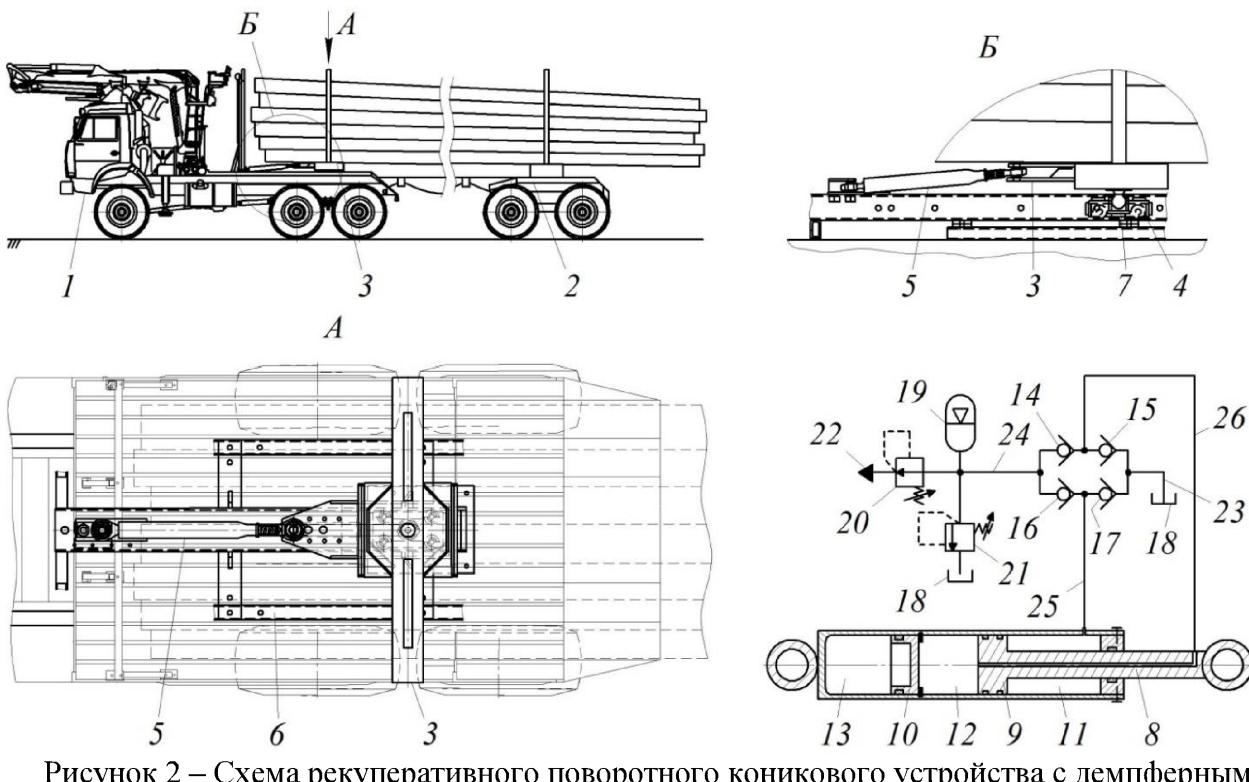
Схема рекуперативного поворотного коникового устройства с демпферным механизмом: 1 – лесовозный тягач; 2 – прицеп-роспуск; 3 – поворотный коник; 4 – механизм перемещения поворотного коникового устройства; 5 – гидроцилиндр; 6 – продольные лонжероны рамы; 7 – шаровая опора; 8 – шток; 9 – поршень; 10 – поршень газовой полости; 11, 12 – штоковая и поршневая полости; 13 – газовая полость; 14-17 – обратные клапаны; 18 – гидробак; 19 – пневмогидроаккумулятор; 20 – редукционный клапан; 21 – предохранительный клапан; 22 – порт подачи рабочей жидкости потребителю; 23 – всасывающий трубопровод; 24 – напорный трубопровод; 25, 26 – гибкие трубопроводы
